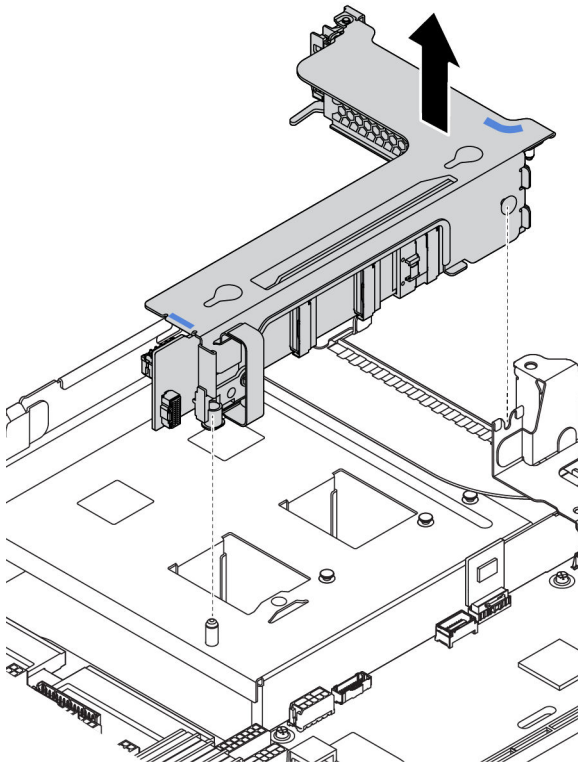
Rimozione dell'assieme verticale 3 (staffa verticale a due slot)
